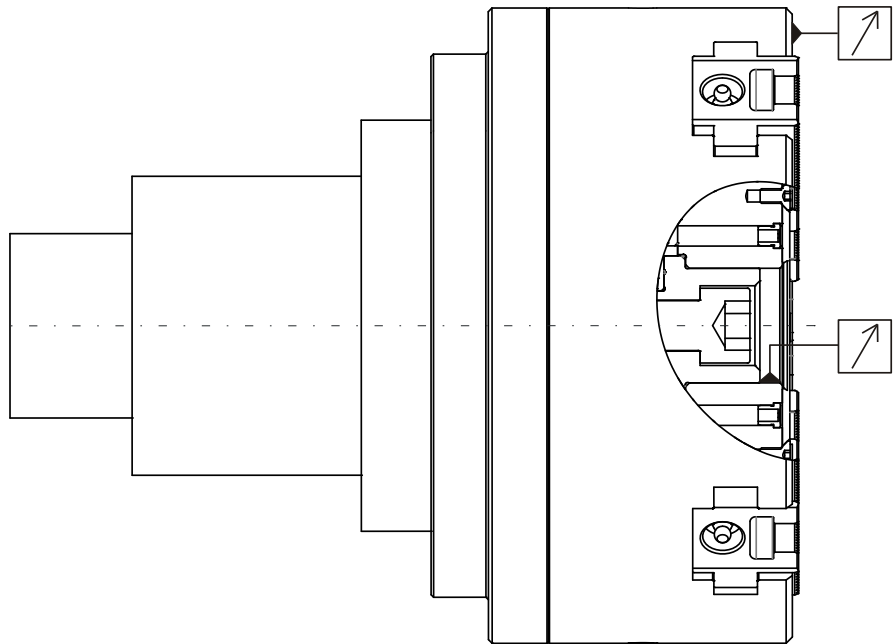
Mandrin de serrage monté sur une bride intermédiaire.
